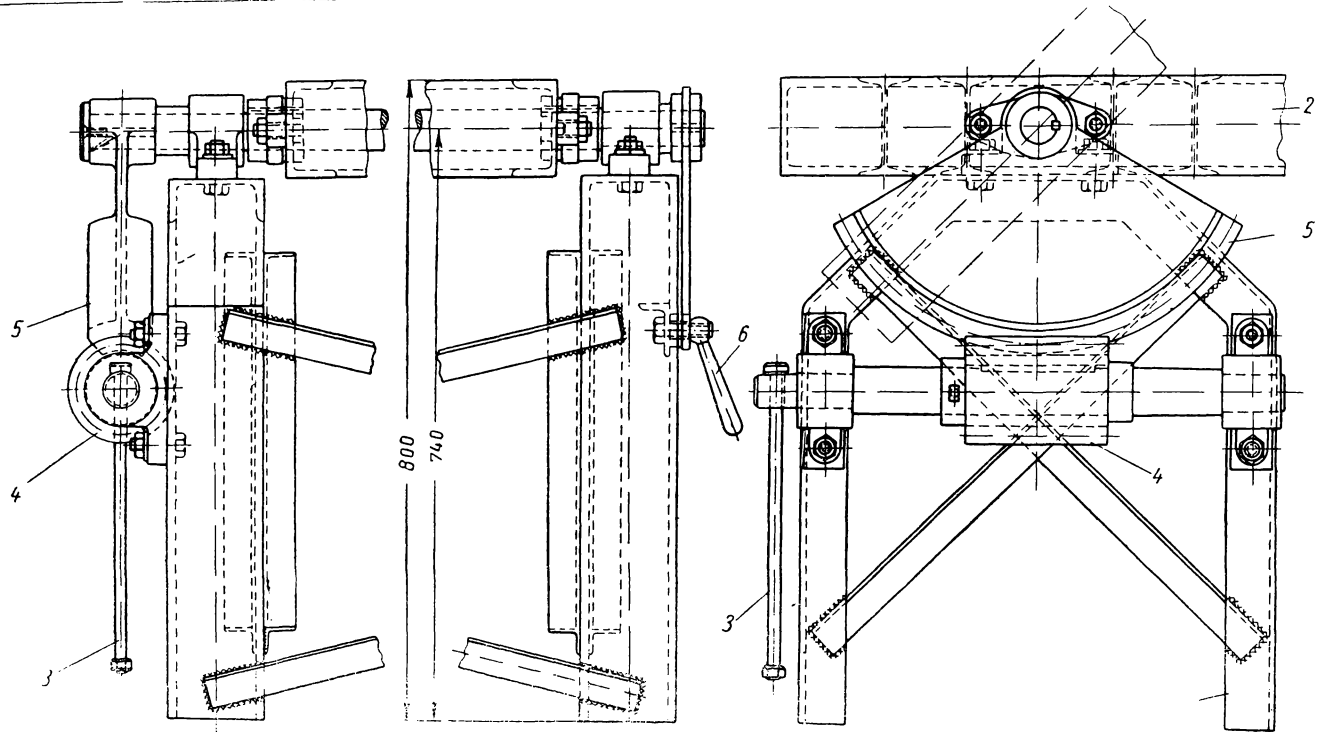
Приспособление для суперфиниша (устанавливается на токарном станке вместо резцовой головки):
